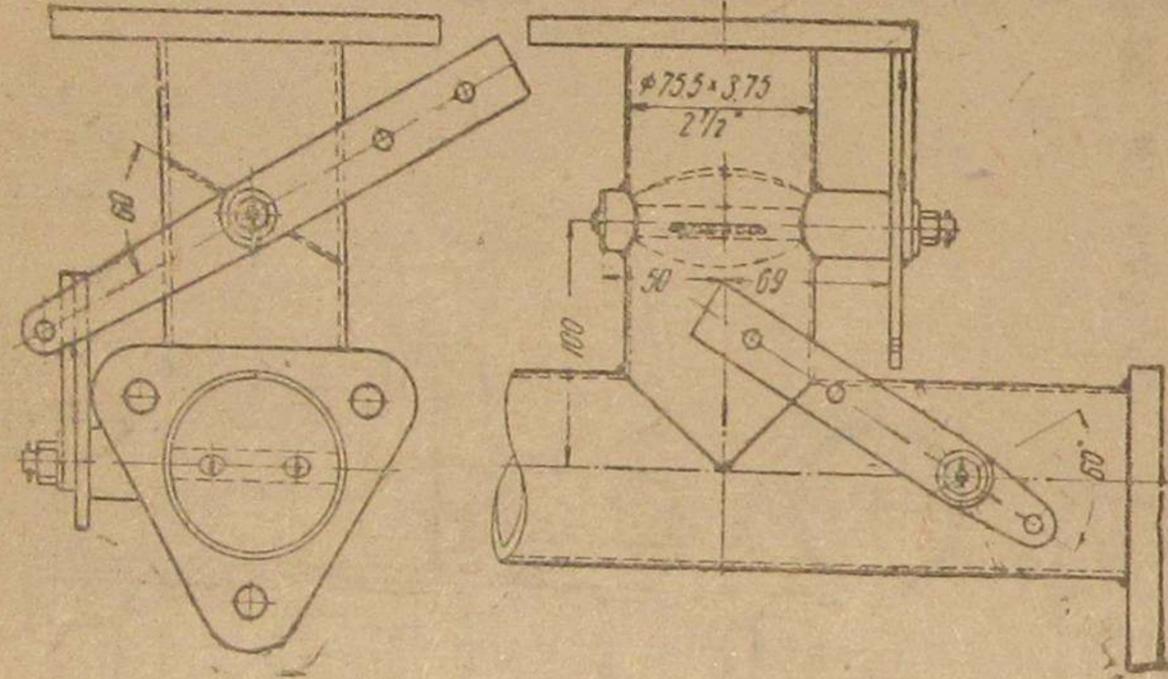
Газовые и воздушные дроссели смесителя для дизеля М-17
